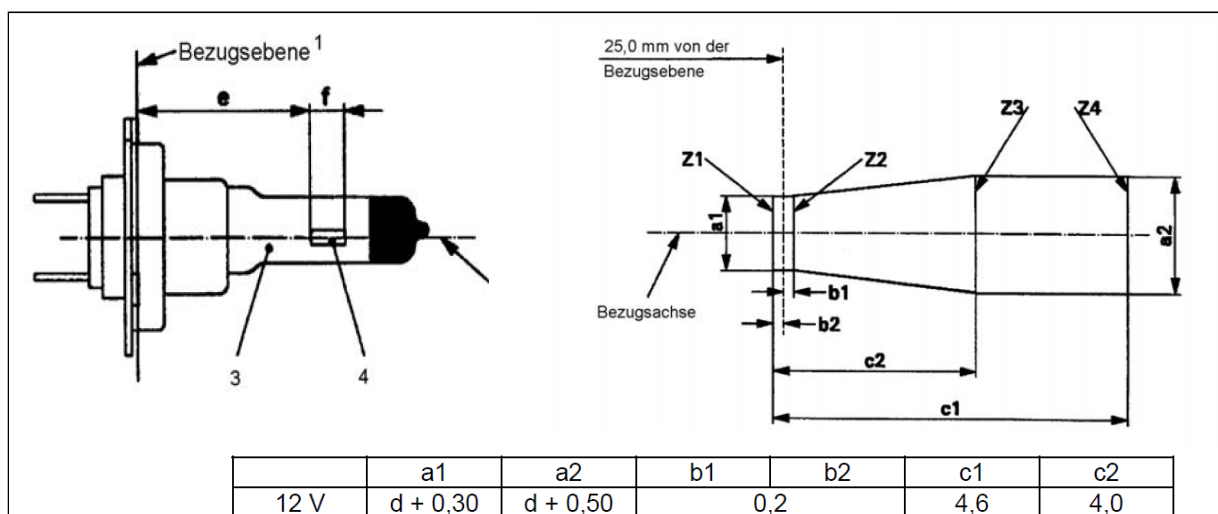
Maße der H7(links) und der Toleranzbox der Wendel (rechts) in mm aus der ECE R37 [Ece05]
